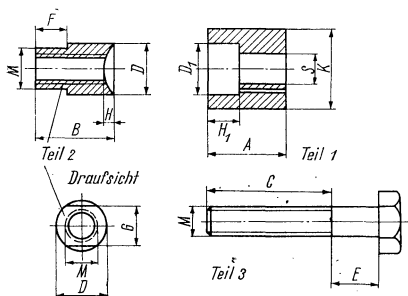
Maßskizze für ein dreiteiliges Stanzwerkzeug
